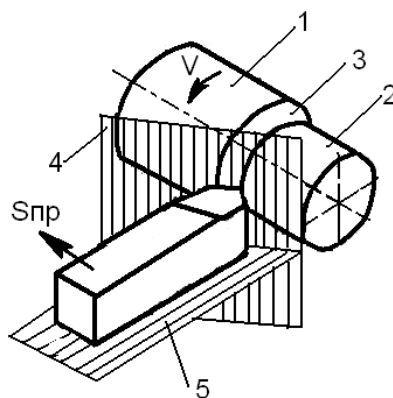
Координатные плоскости и поверхности обрабатываемой заготовки (1 – обрабатываемая поверхность; 2 – обработанная поверхность; 3 –
